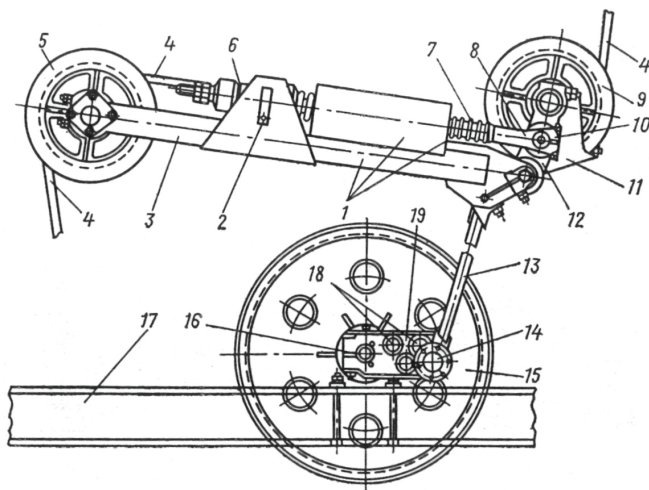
Ударний механізм станка УГБ-ЗУК:
